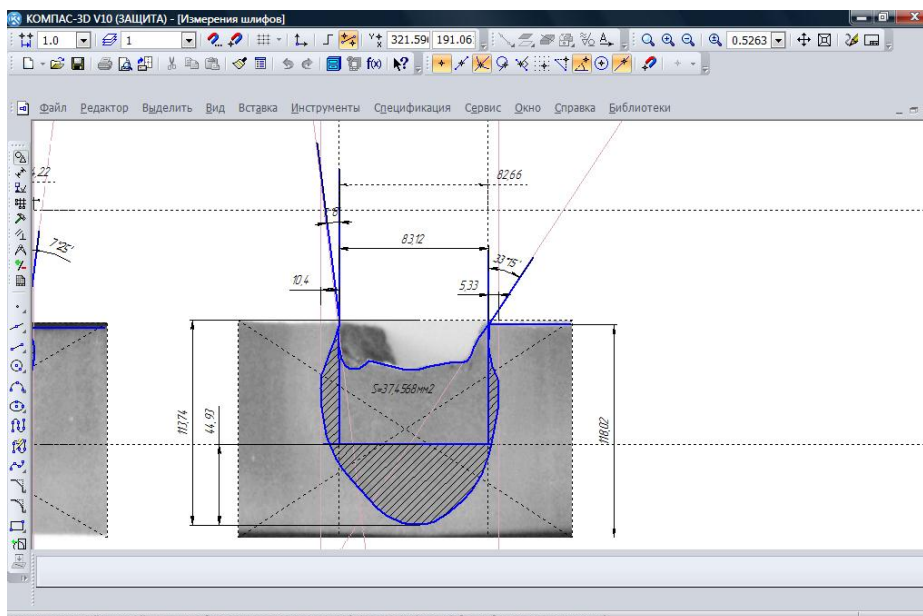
Лист программы «Компас 3D-V10» с макрошлифом сварного соединения и поставленными геометрическими размерами
